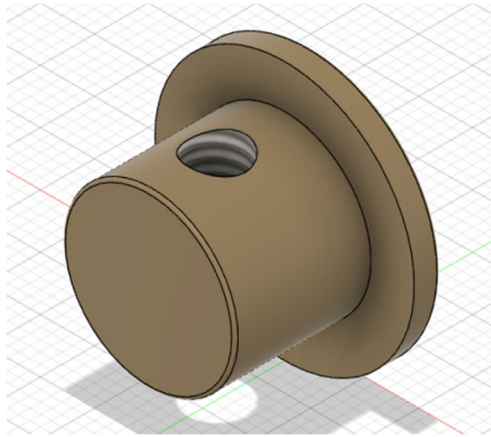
3D-модель гайки коромисла гальмівної системи
